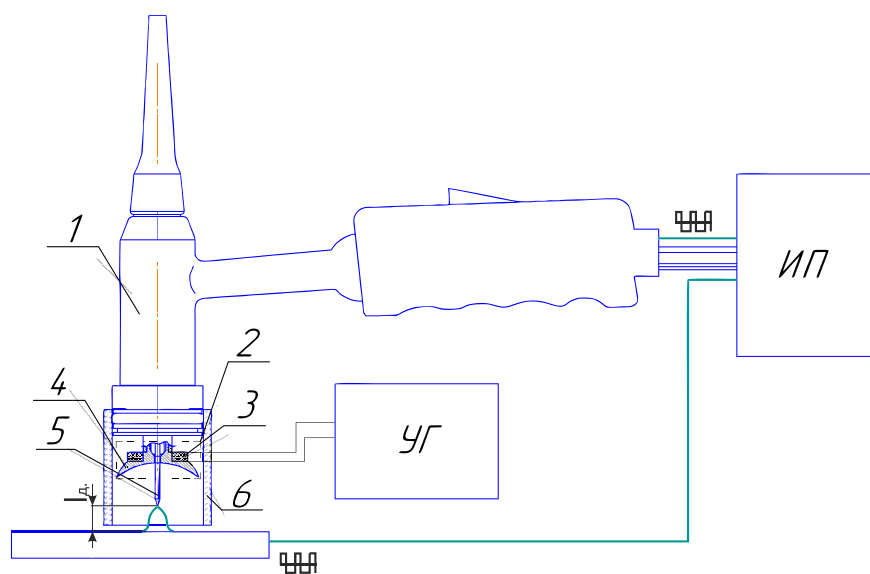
Устройство для сварки неплавящимся электродом с применением ультразвуковых колебаний: 1 – сварочная горелка; 2 – пьезоэлектрический преобразователь; 3 – пьезокерамический элемент; 4 – плосковогнутая фокусирующая линза; 5 – неплавящийся электрод; 6 – защитное сопло;  $l_d$  – длина дуги
